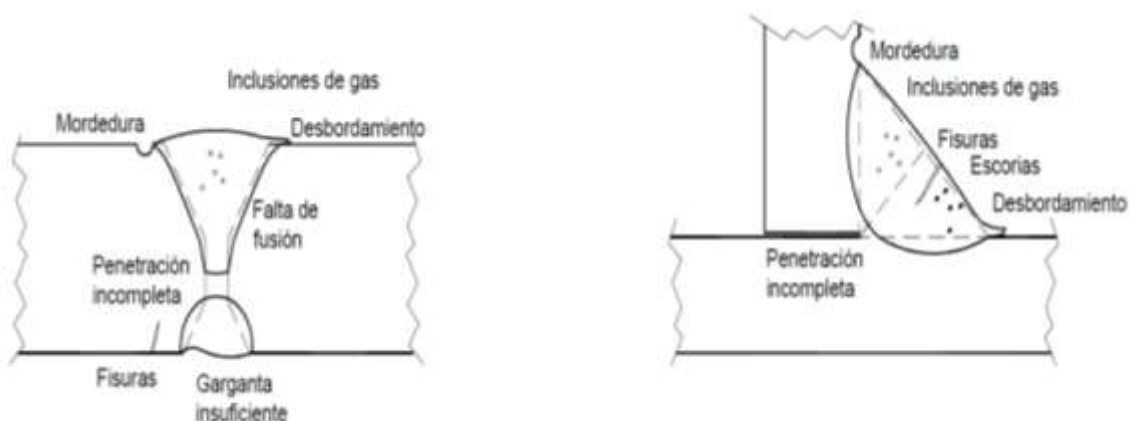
Defectos en soldadura a tope y de Angulo
